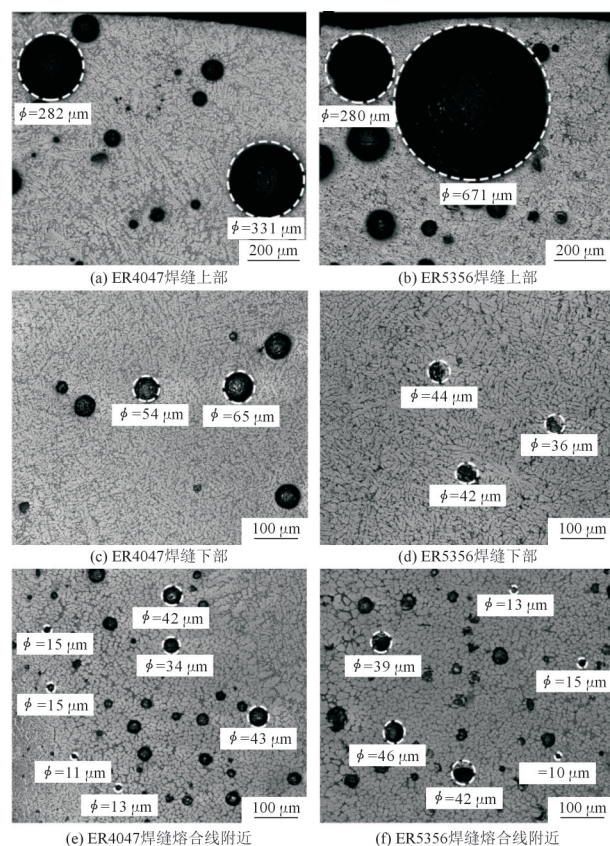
AlSi7Mg 合金 CMT 焊接产生的孔隙形貌^[16]
